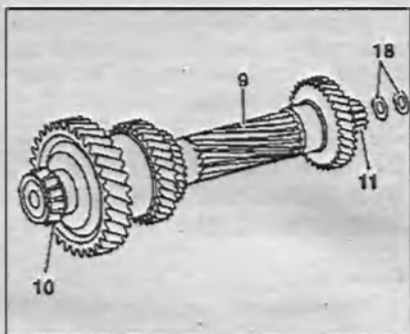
Смажьте конические подшипники 10 и 11, перед установкой зафиксируйте смазкой регулировочные шайбы 18 промежуточного вала 9.
